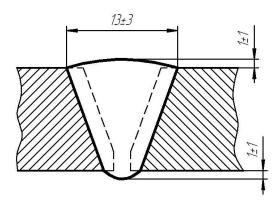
Геометрия получившегося при сварке шва
